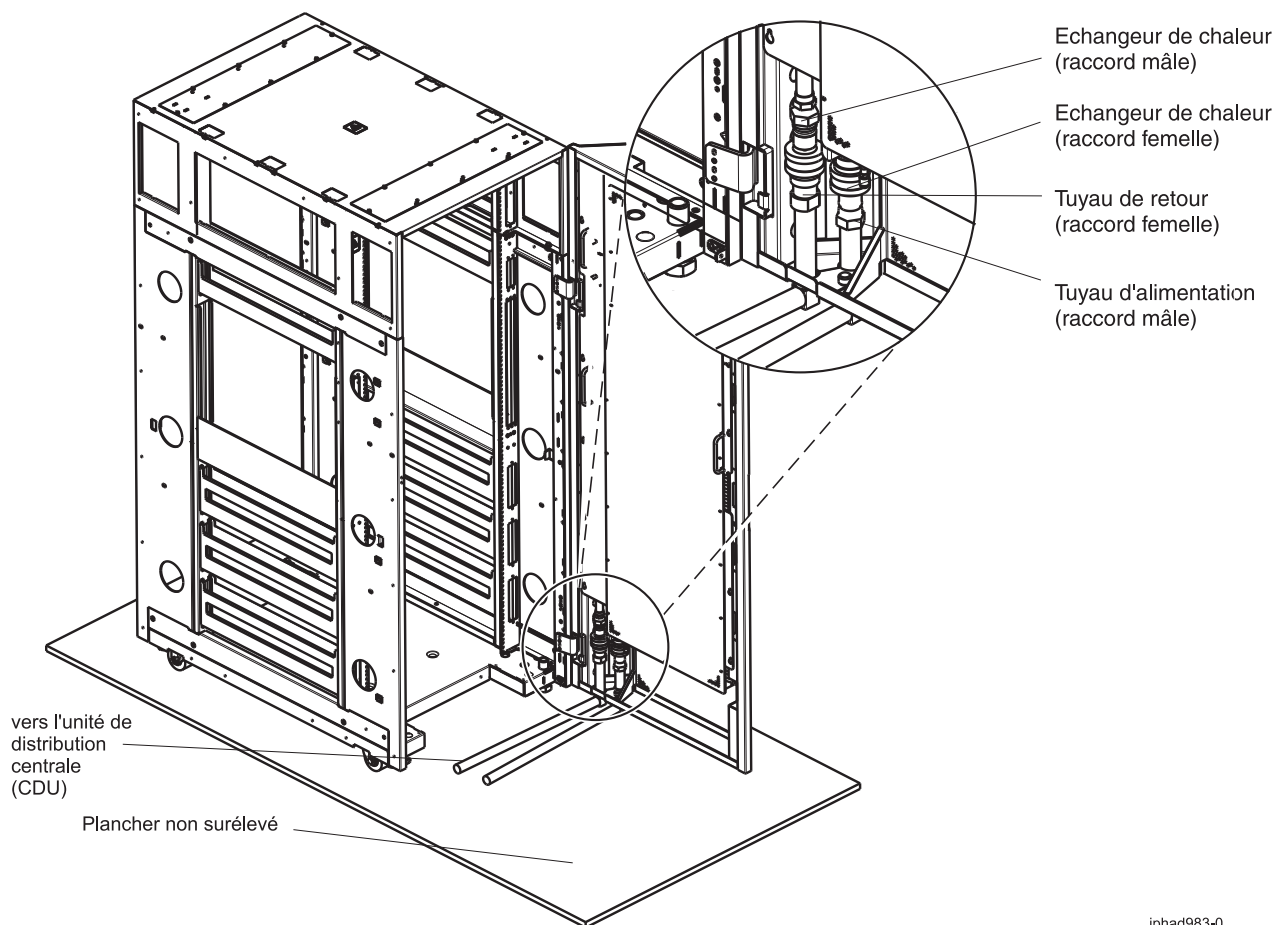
Disposition des tuyaux pour une armoire à rails EIA 24 pouces sans faux plancher
